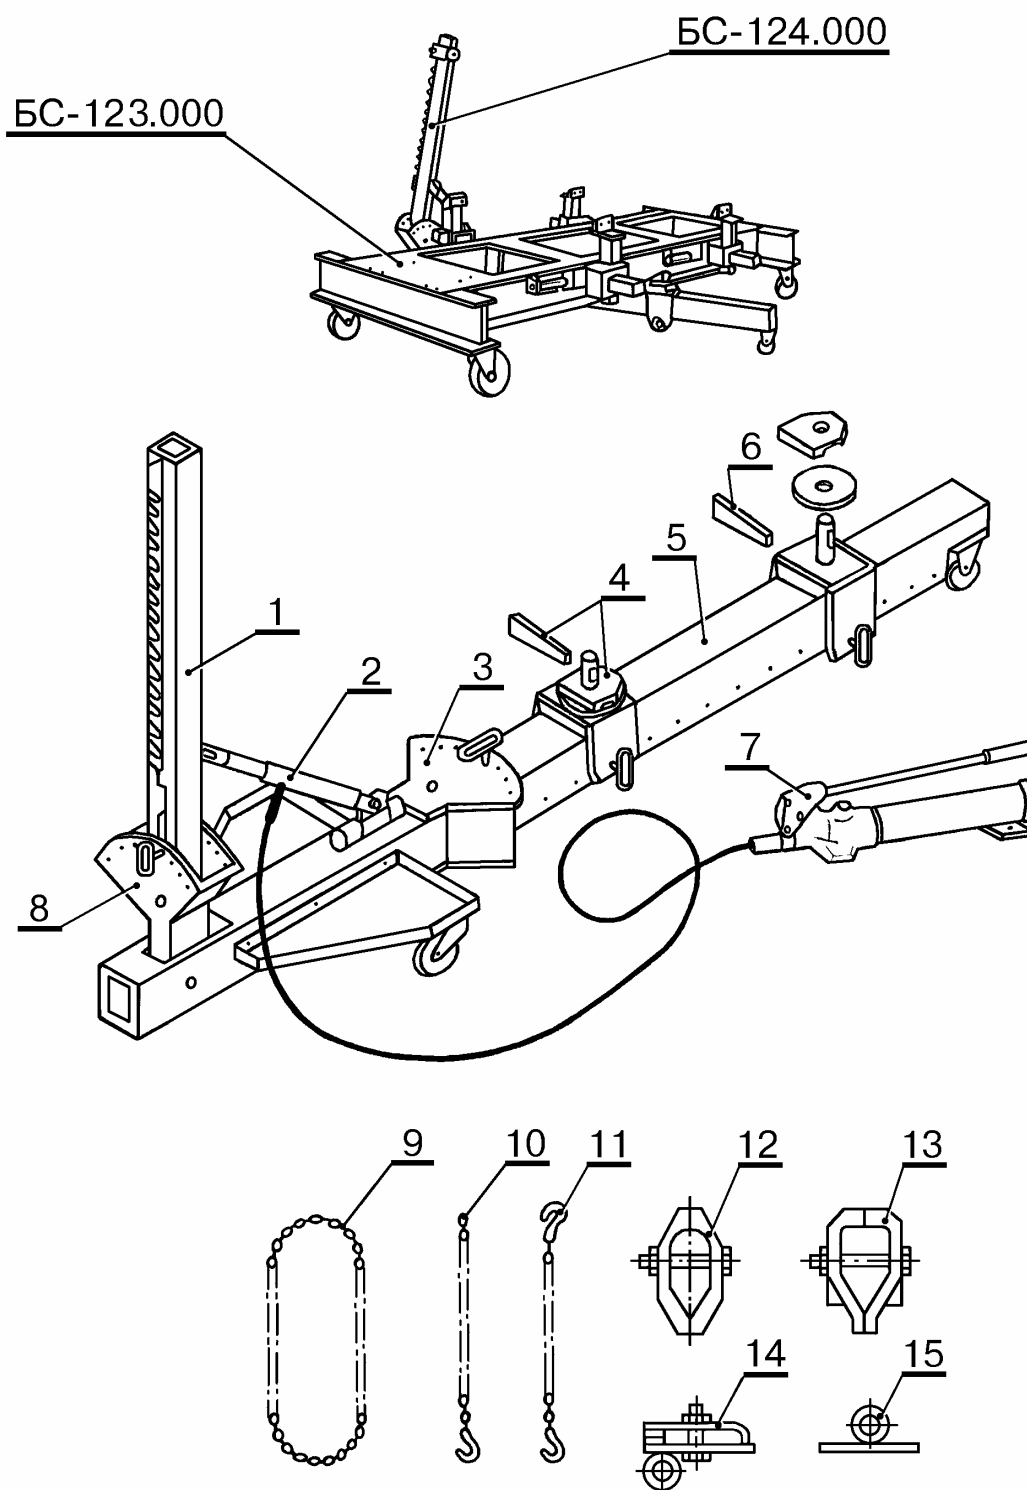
Общий вид устройства для правки кузовов БС-124.000 со стандом БС-123.000:
